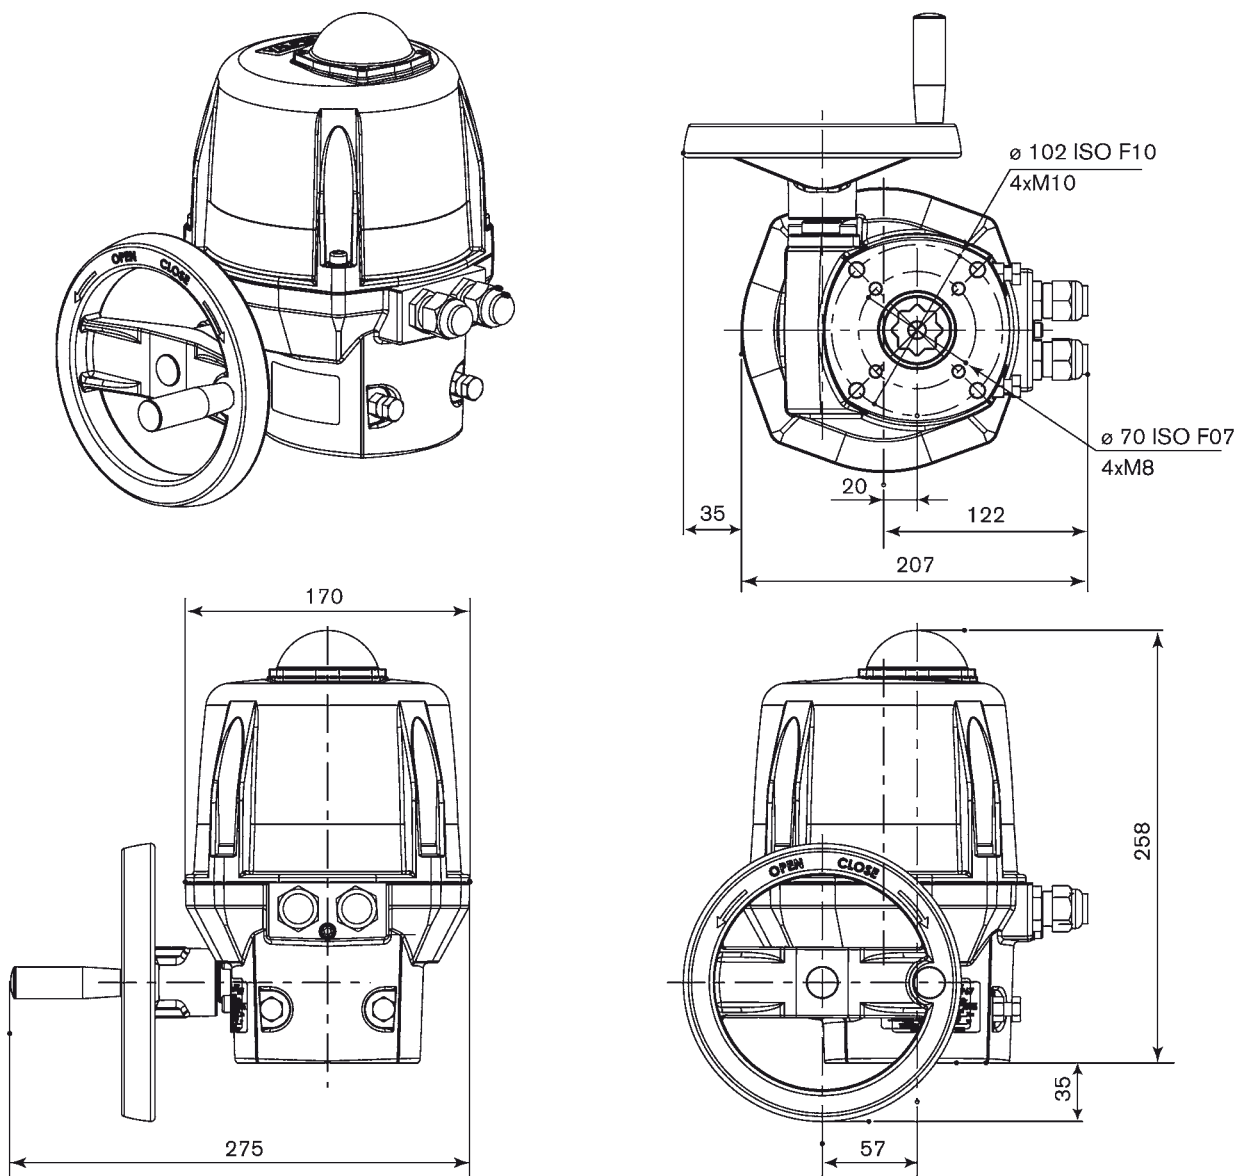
Dimensions type 3005 avec couple de serrage 100 - 300 Nm
